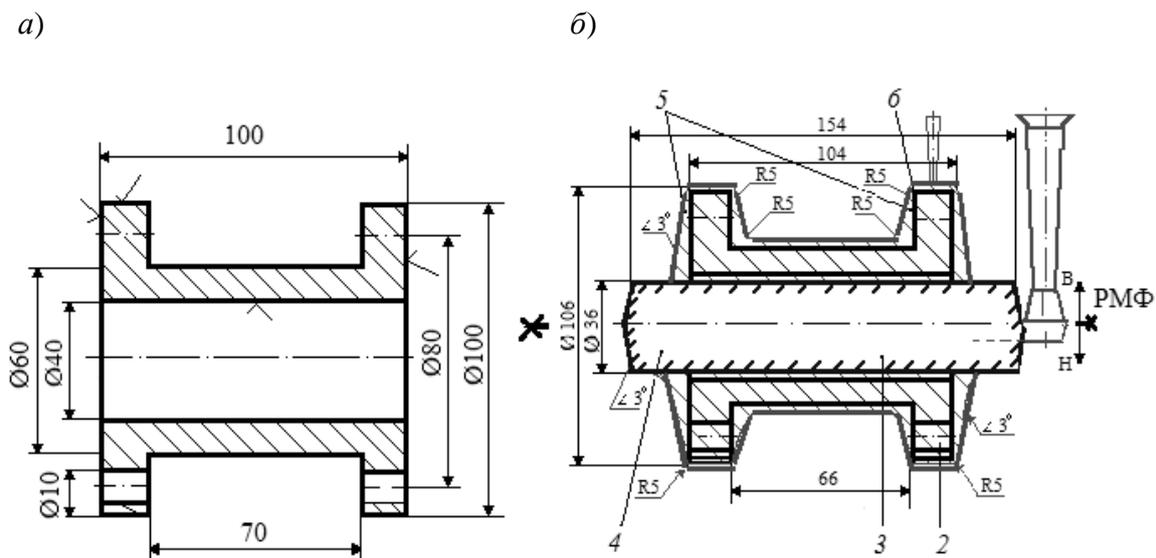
Эскизы детали (а) и технологического чертежа отливки (б)
